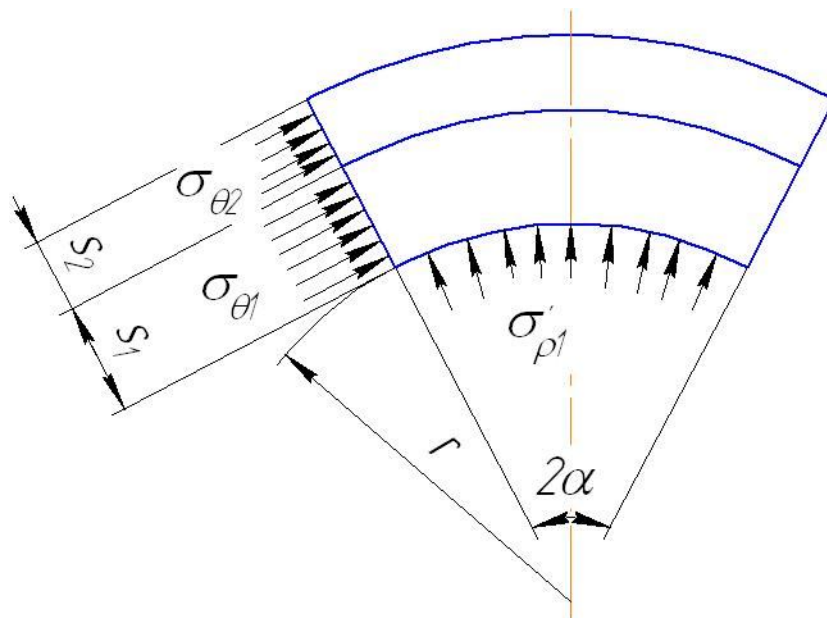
Схематичне зображення елемента заготовки під час згинання
